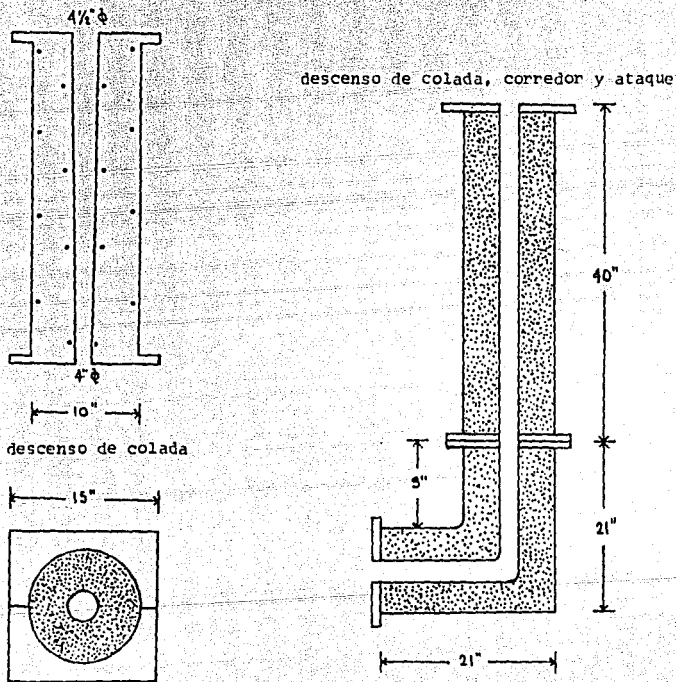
Componentes del Sistema de Colada y sus dimensiones.
